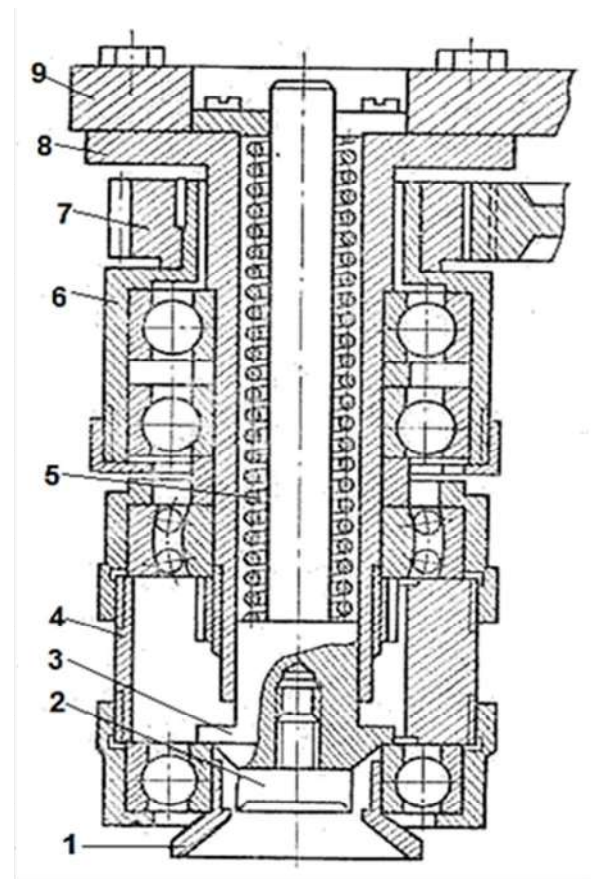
Обкочувальний патрон машини ВУУ-0,5: 1 – конус-центратор; 2 - натискна п'ята; 3 - підпружинений шток; 4 - ексцентрикова втулка; 5 - пружина; 6 - верхня втулка; 7 - привід; 8 - корпус; 9 - карусель машини.
